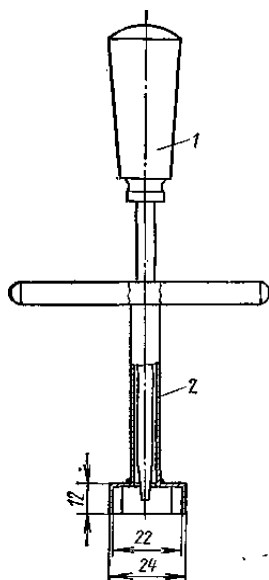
Инструмент для-регулировки клапана второй ступени редуктора:
